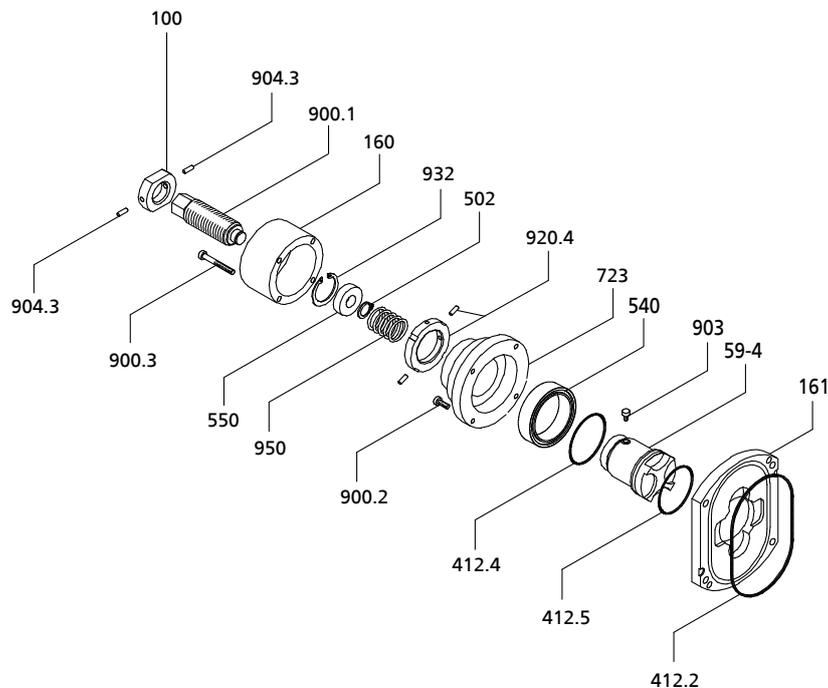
Mechanisches Überdruckventil (Explosionszeichnung)
